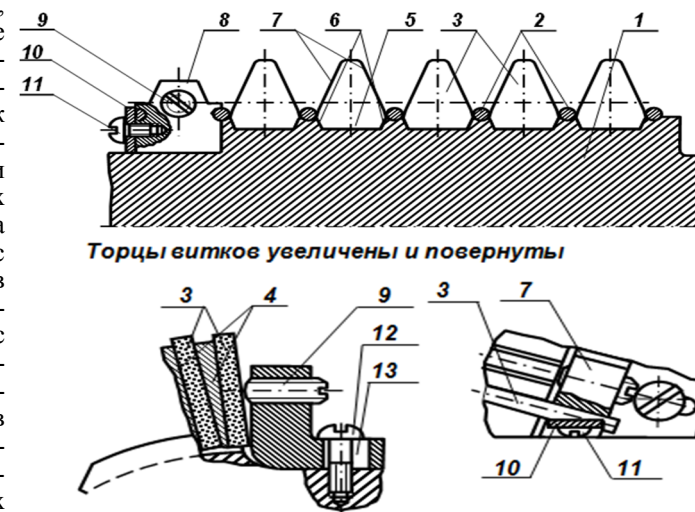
Конструкция сборного червячного зуборезного инструмента с креплением витков, набранных из сменных режущих пластин и клиновидных вставок – пружинами, расположенными у ножек между этими витками
